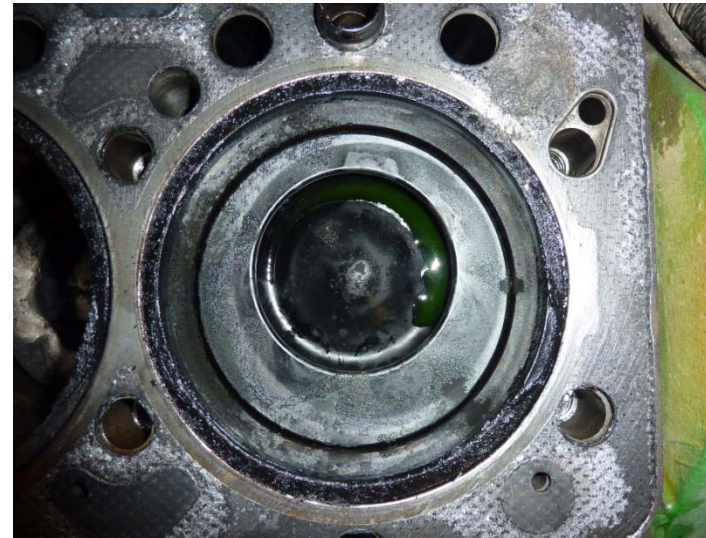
bis 27: Zylinder 6, Einspritzstrahlbilder auf Kolbenboden, Laufbuchse mit Honung und Feuersteg
